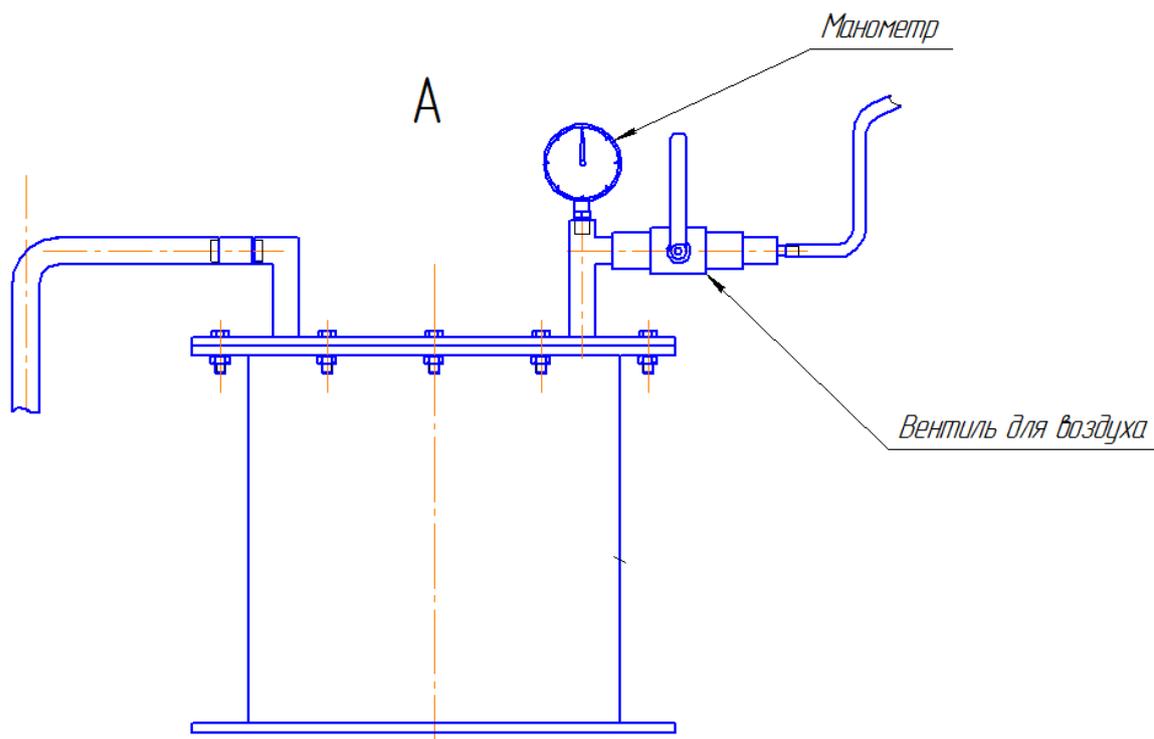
Резервуар установки прокачки тормозной системы
